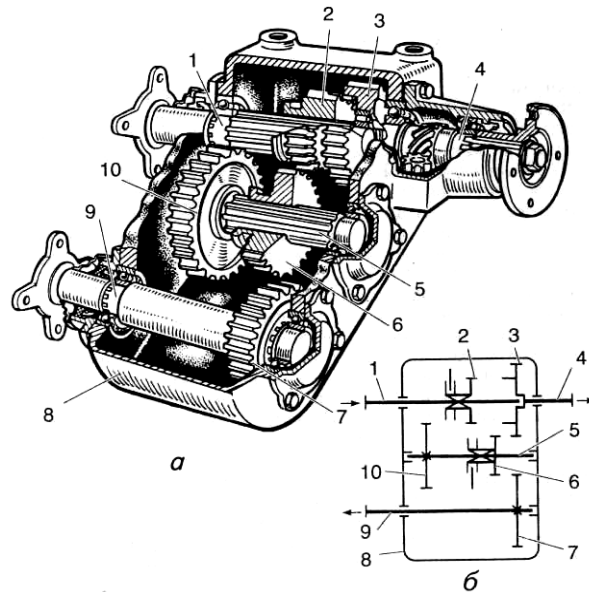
Роздавальна коробка з прямою та знижувальною передачами: а – загальний вигляд; б – кінематична схема; 1 – ведучий вал; 2, 3, 6, 7, 10 – шестерні; 4 – ведений вал; 5 – проміжний вал; 8 – корпус; 9 – вал привода переднього моста
